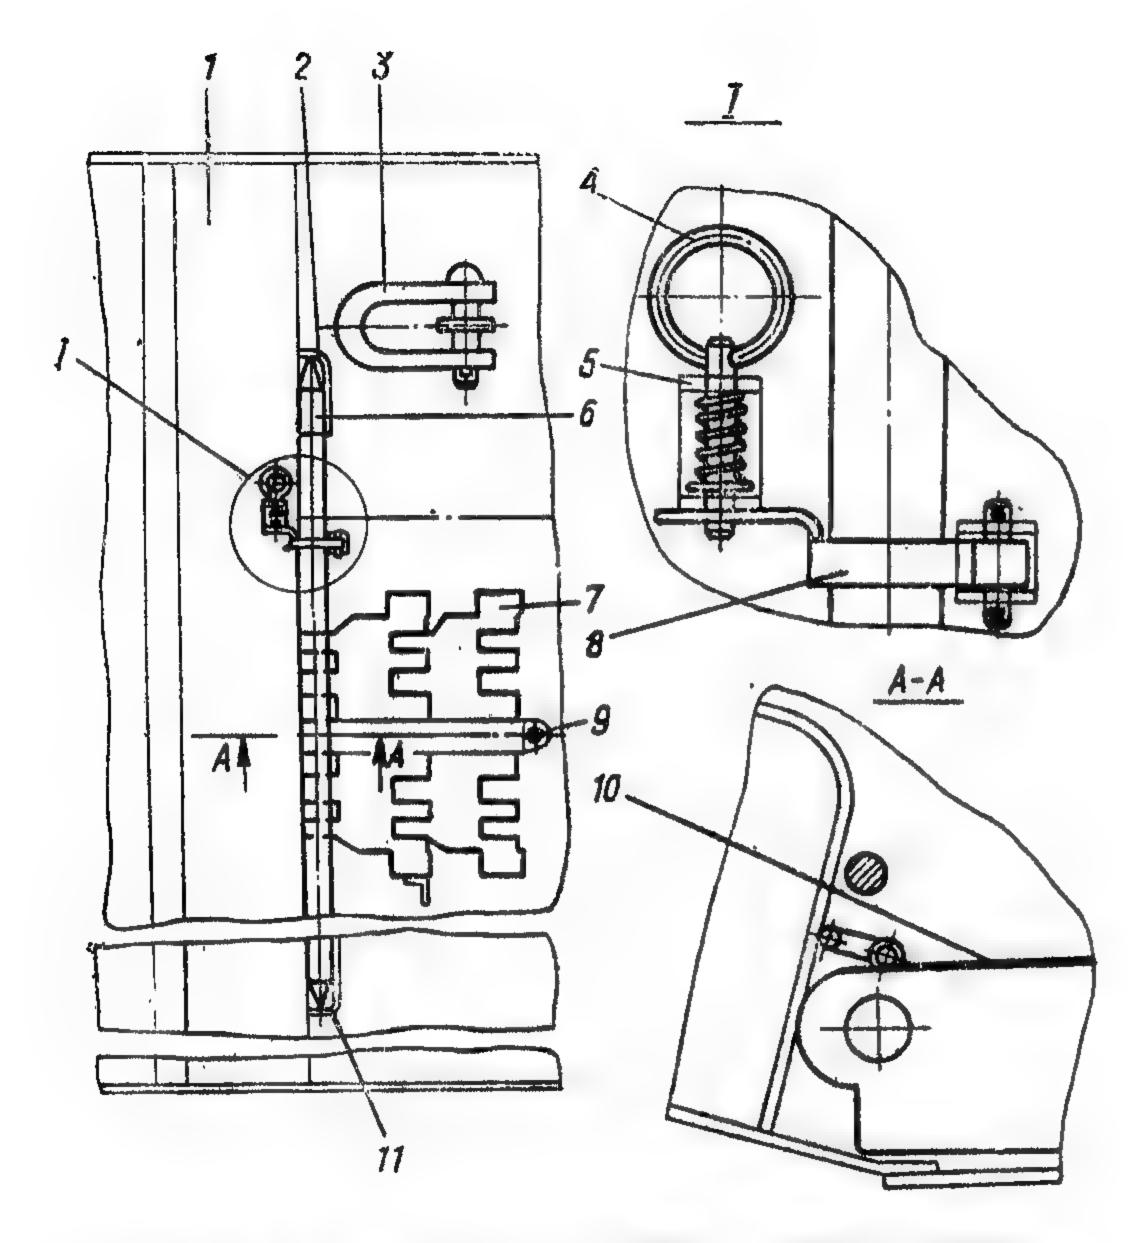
Установка лома, звеньев гусениц и серьги: 1— балка: 2, 5, 11— кронштейны; 3— серьга соединительная; 4— фиксатор; 6— лом; 7— звено гусеницы; 8— скоба; 9— болт; 10— лента
